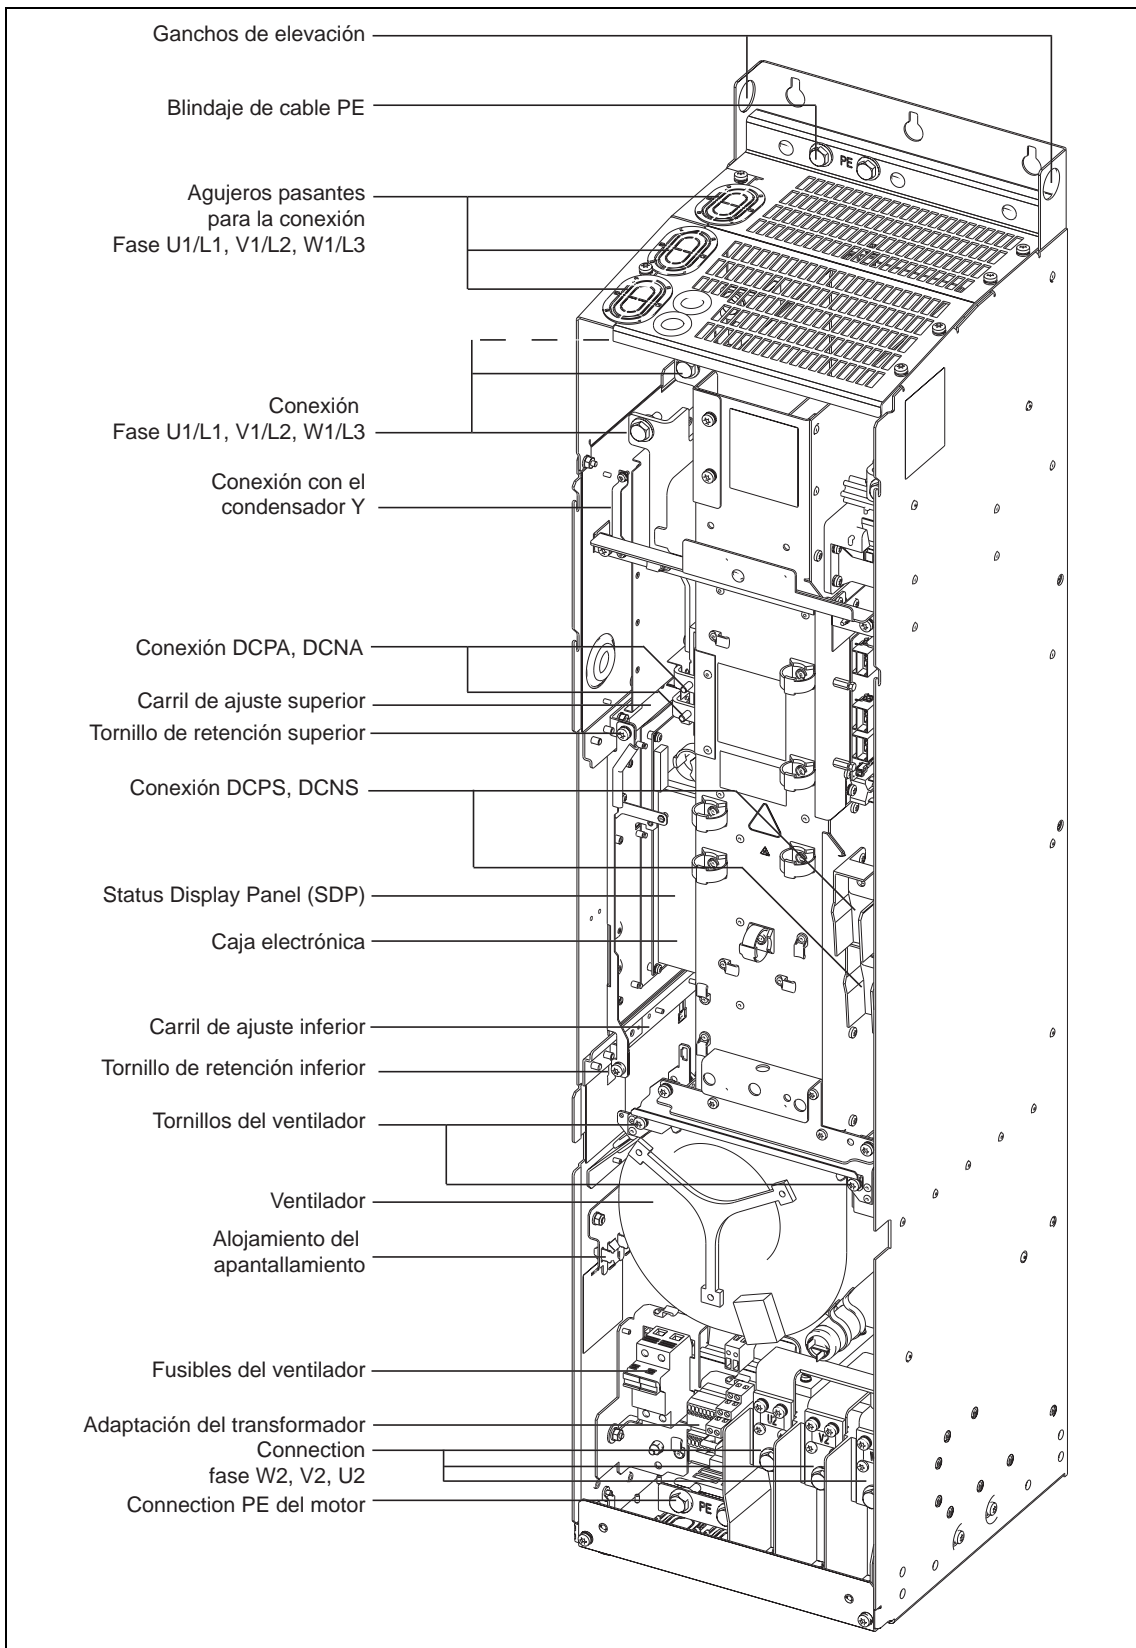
Vista general de las conexiones, tamaño constructivo FX
